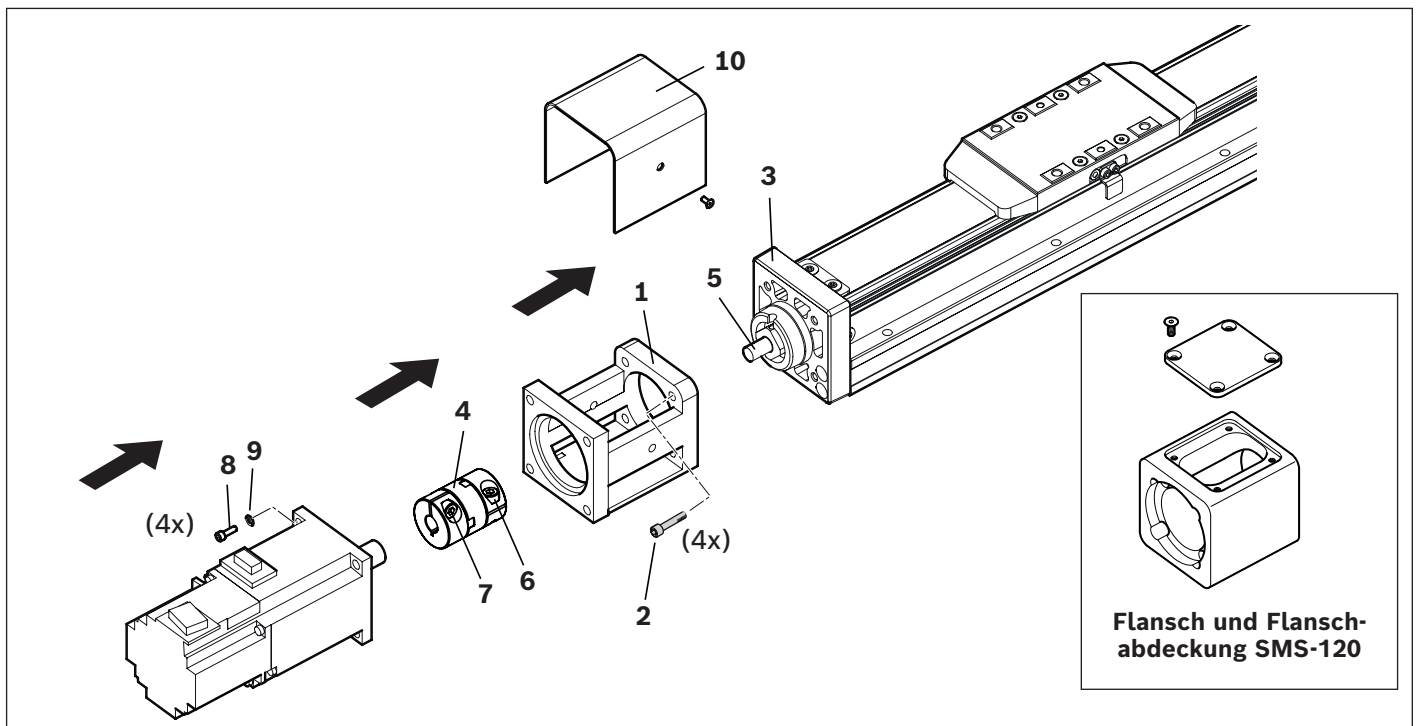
Motor mit Flansch und Kupplung montieren (SMS-040 – SMS-120)
